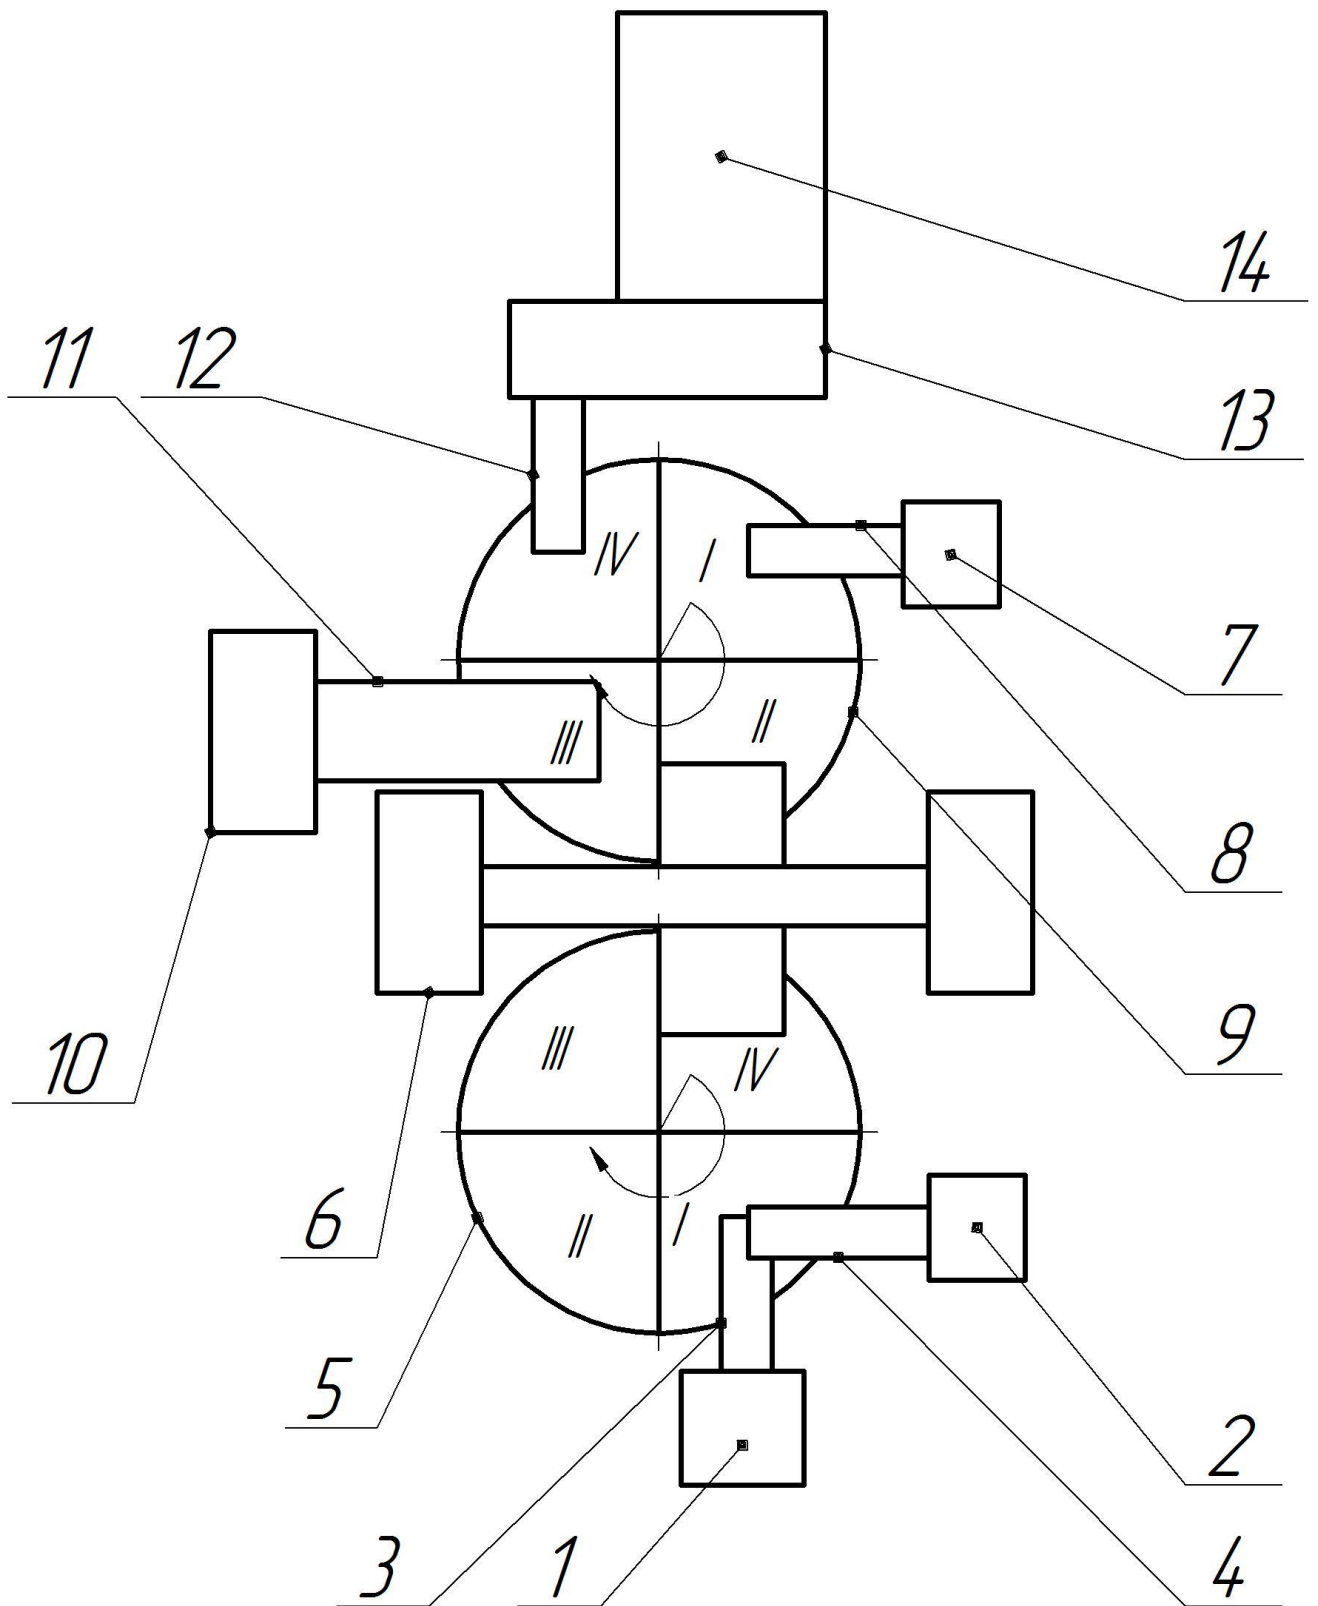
Общй вид робототехнического комплекса для упаковки сцеплений
